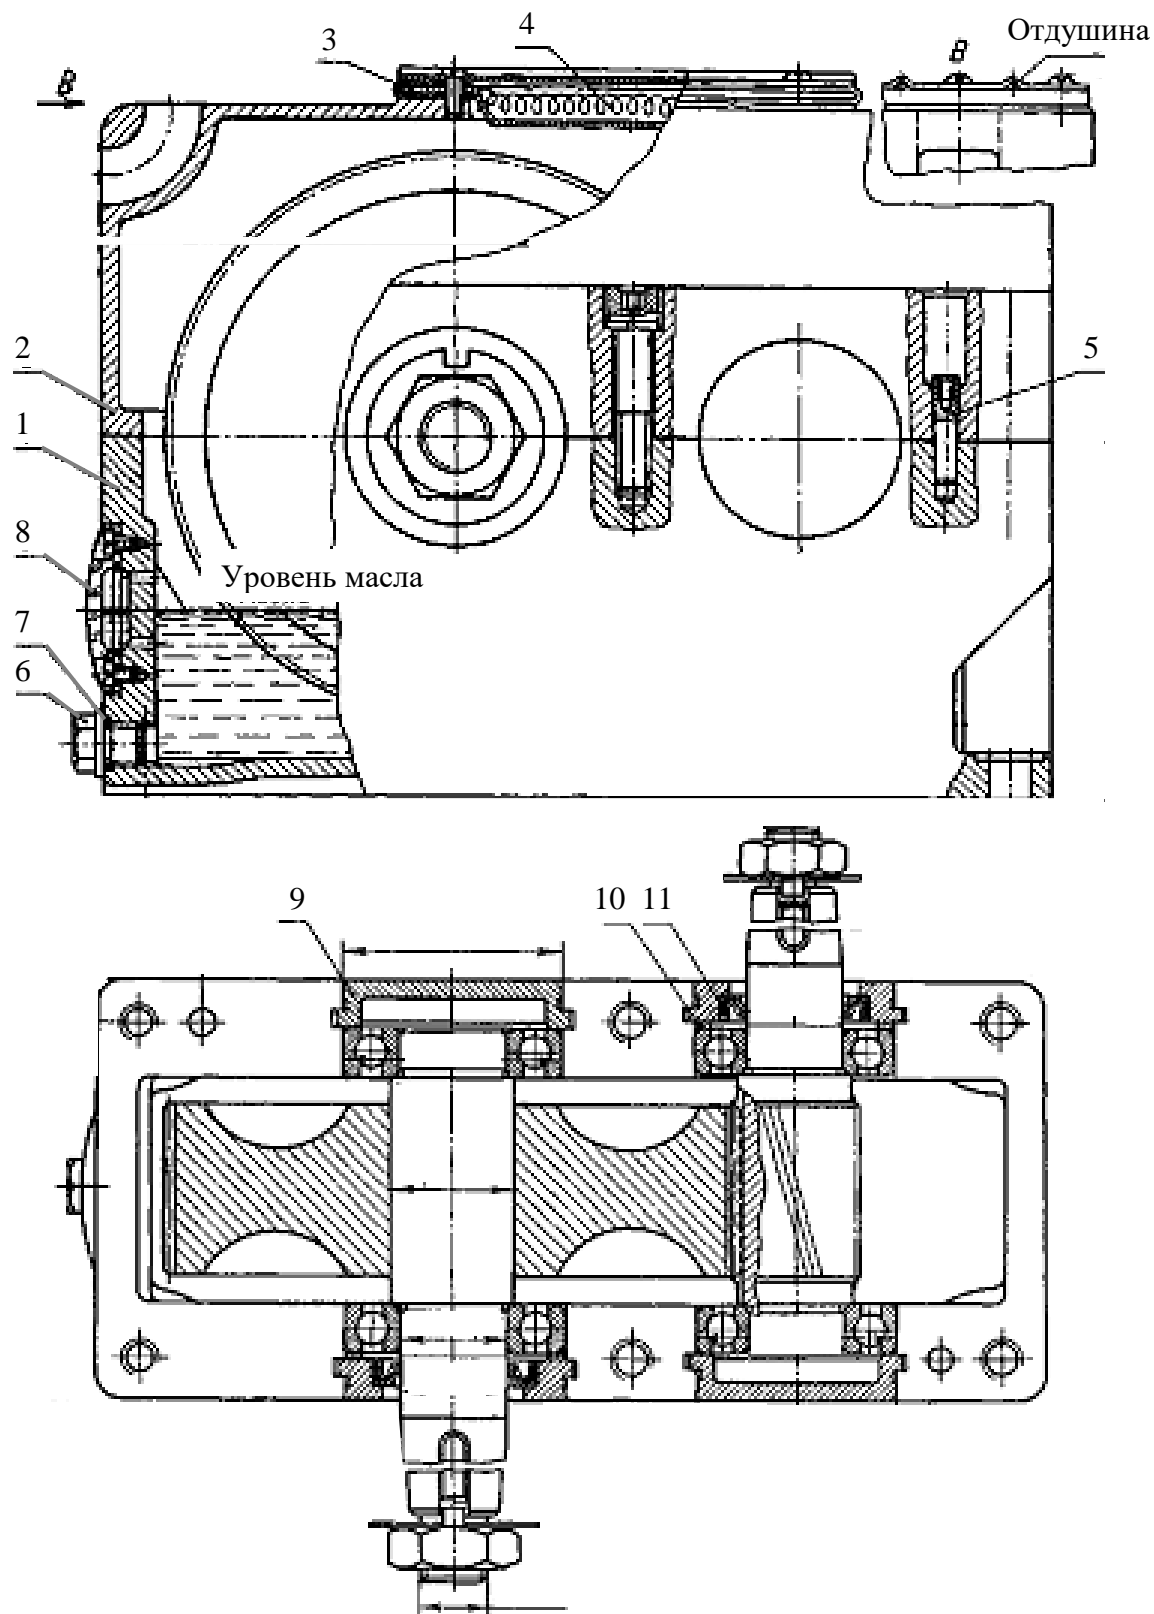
Редуктор цилиндрический одноступенчатый:
